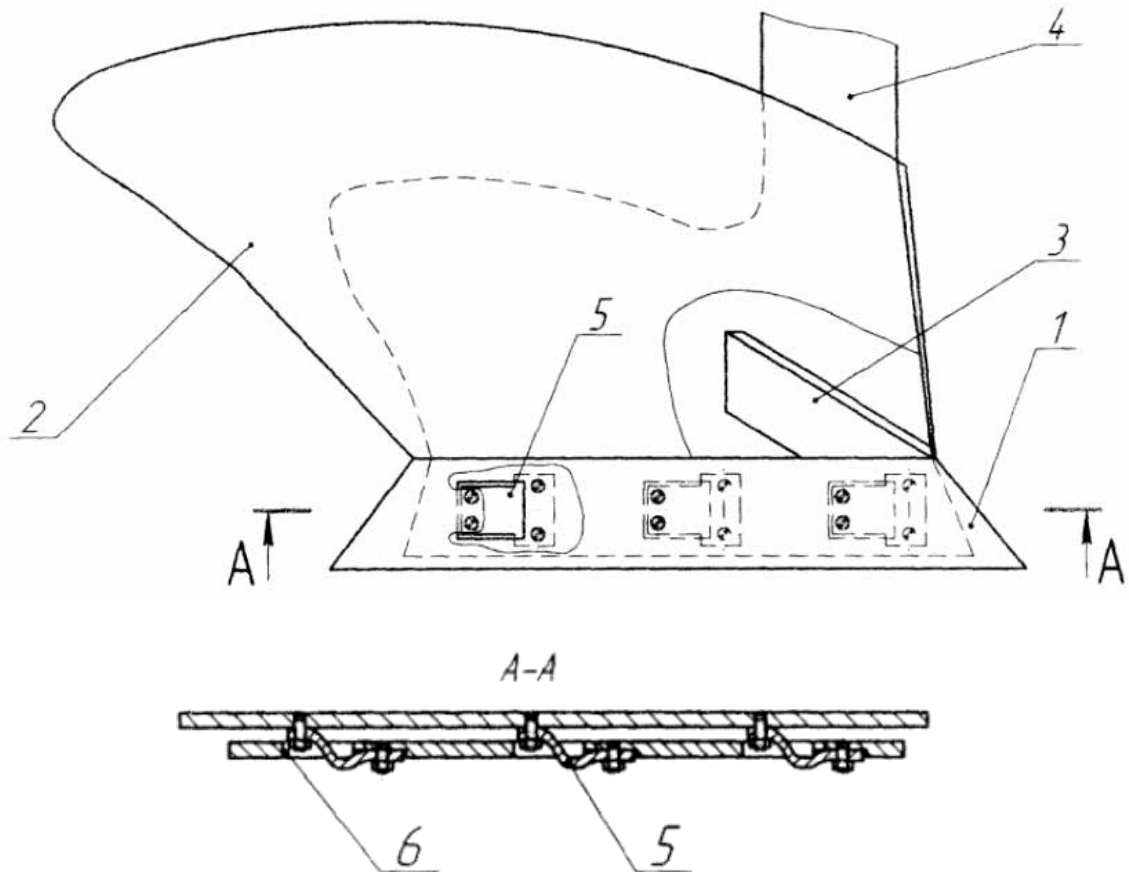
Корпус плуга з підпружиненим лемішем [6]
